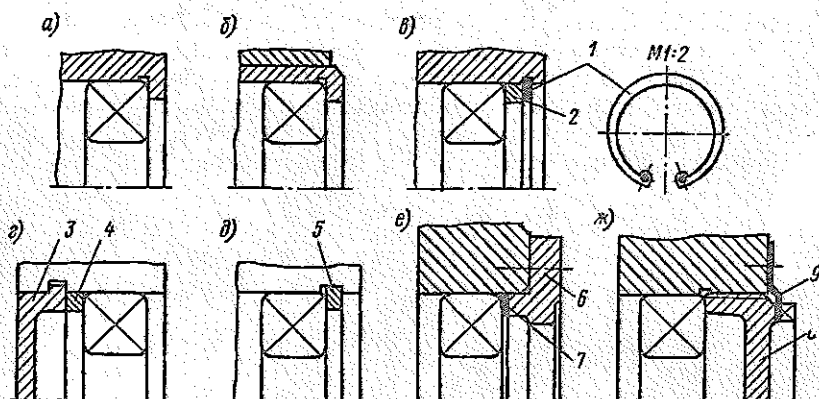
Упорные бурты в корпусе для наружных колец подшипников
